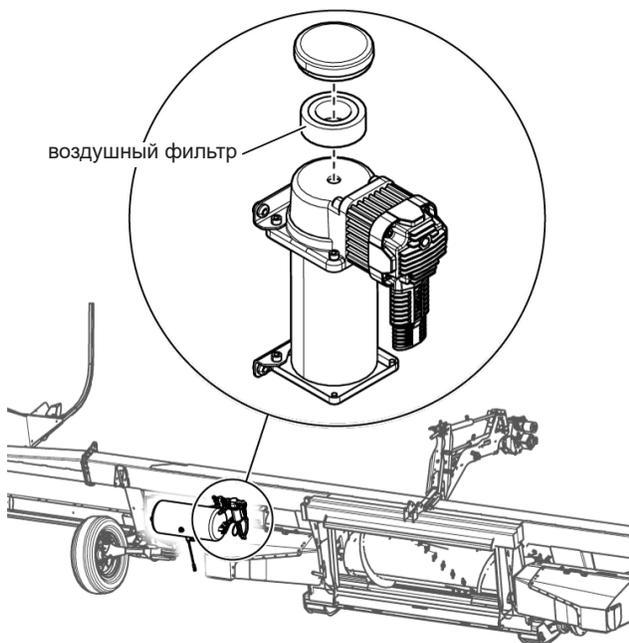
Впускной воздушный фильтр воздушного компрессора
